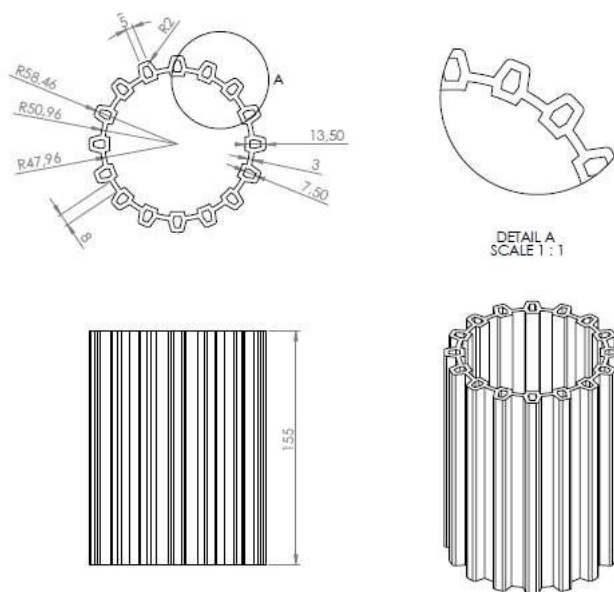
Desenho de representação 3D de um dos cinco objetos da Coleção Gears.
